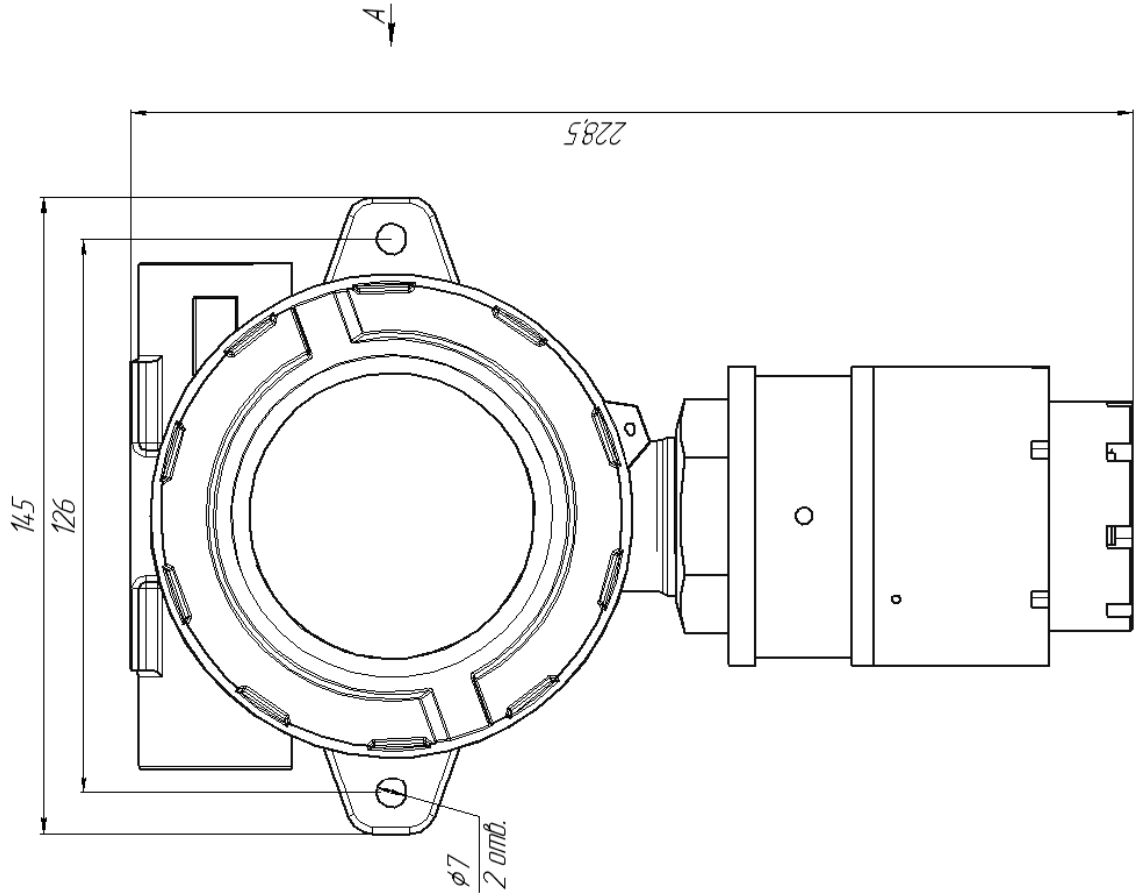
Габаритный чертеж ДГС ЭРИС-210
